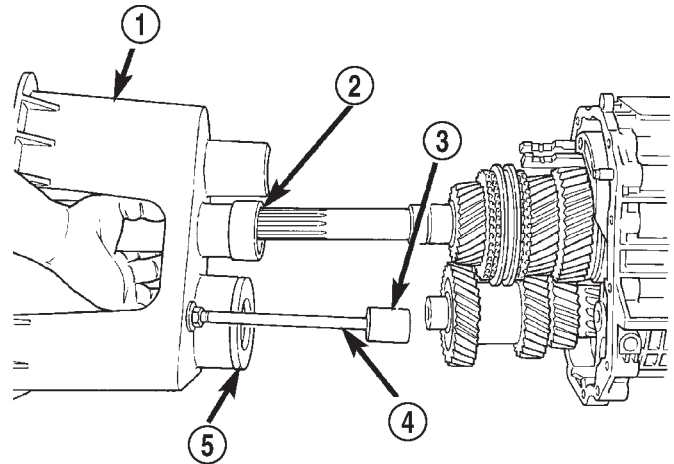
CONJUNTO DE HORMA DE MONTAJE
